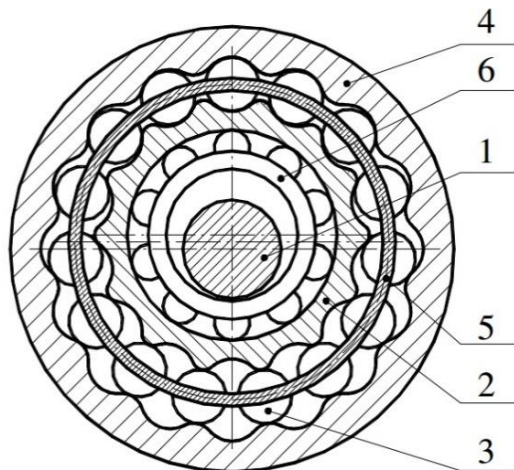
Схема передачи с ПТК и свободной обоймой:
